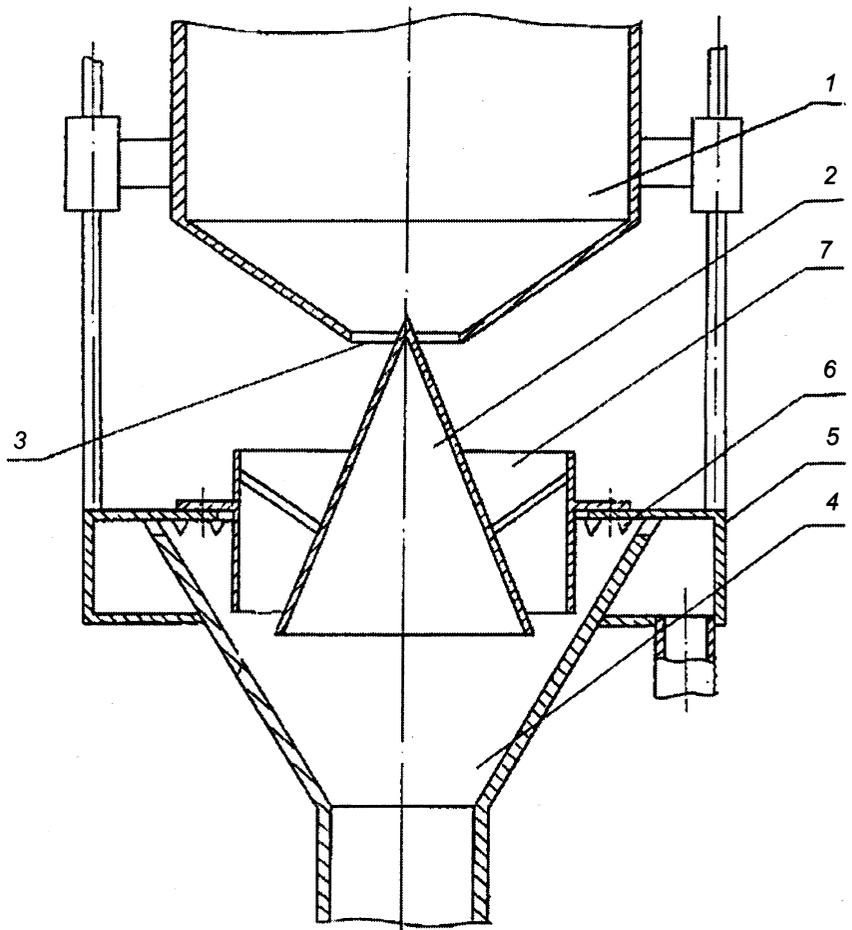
Дозирующее устройство для приготовления суспензии: 1 — бункер порошкообразного материала; 2 — конус-рассекатель; 3 — узел подачи; 4 — коническая приемная воронка; 5 — кольцевой коллектор; 6 — отверстия в стенке коллектора; 7 — цилиндрическая обечайка
